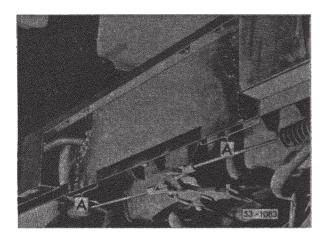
Reststücke des Anschlußflansches in den Bereichen "A" entfernen (Auflage für Verstärkungsbleche)
